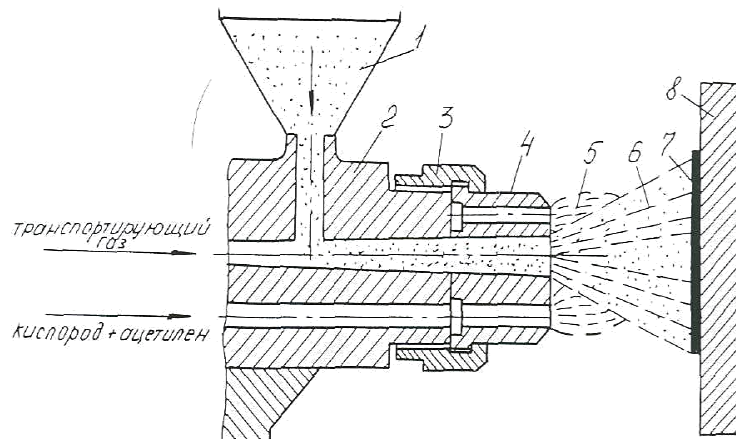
Схема газопламенного напилення з розпиленням порошку:
